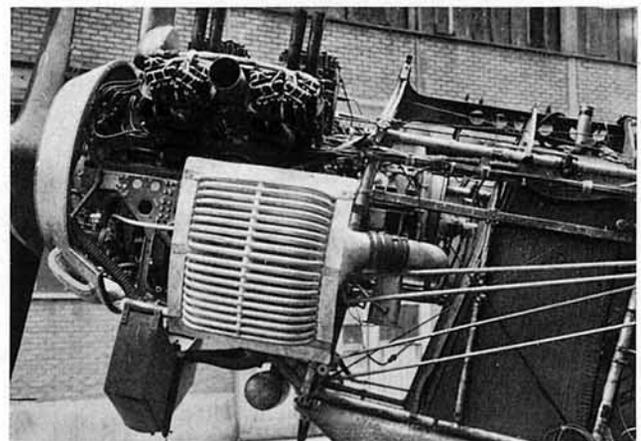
Compresor Rateau de mando mecánico, instalado sobre motor Farman 12 WE, 500 cv.
